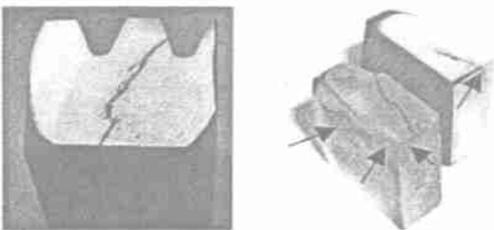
齿轮端面裂纹宏观形貌 (箭头所指处为深入内部的裂纹)
